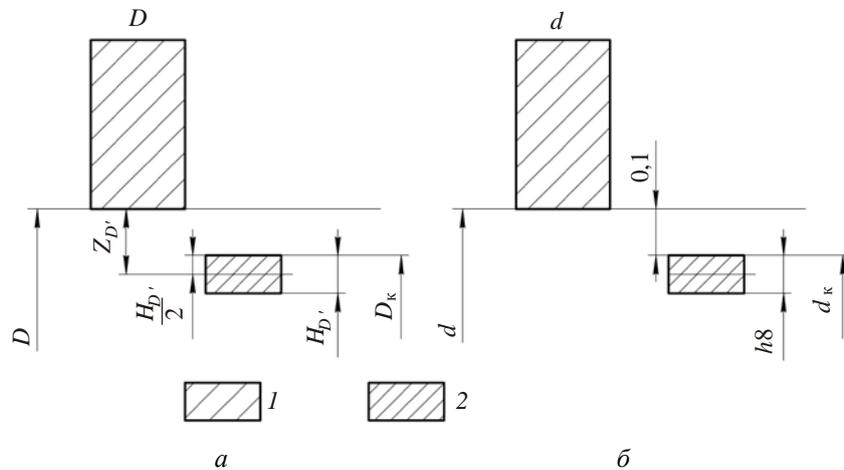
Схемы расположения полей допусков калибров-пробок для нецентрирующих диаметров D и d
